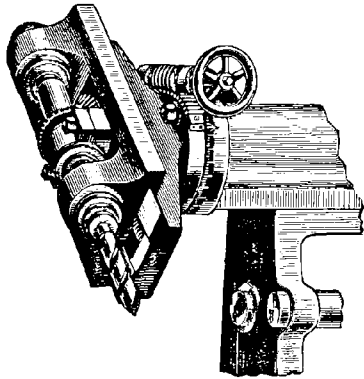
Disposition pour fraiser ou percer obliquement.
